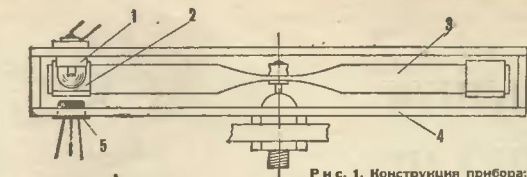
Конструкция прибора: 1 — лампочки, 2 — полоски фольги, 3 — стрелка, 4 — корпус, 5 — фототранзисторы.
